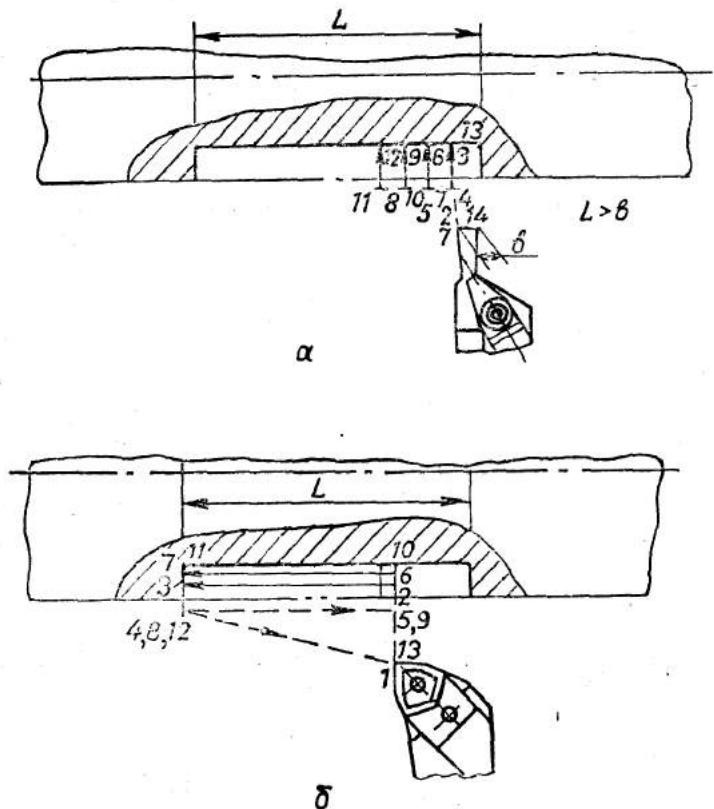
Схема послідовної обробки широкої канавки про-
